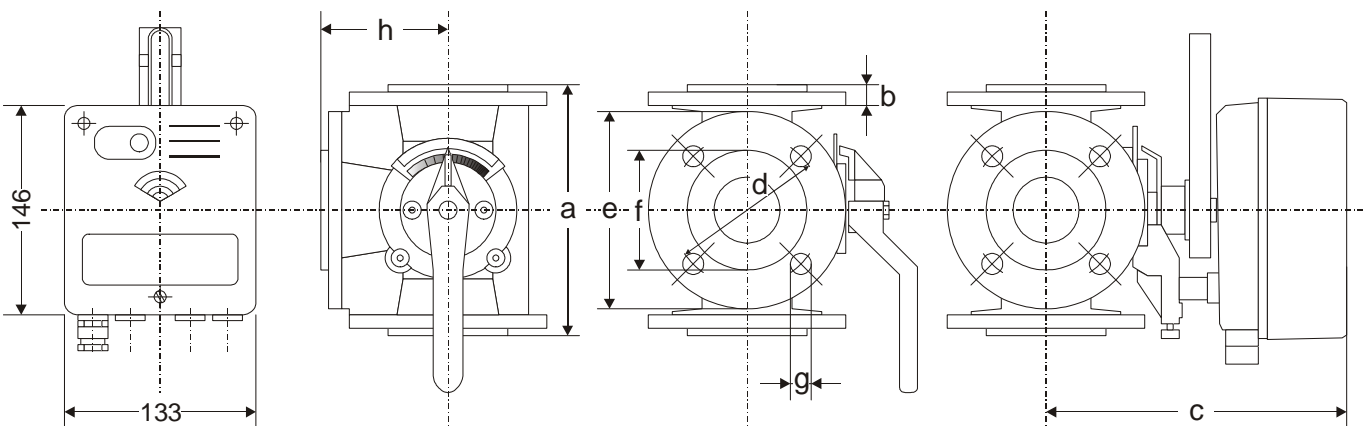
VMM et DRxxxGFLA, dimensions (en mm)
